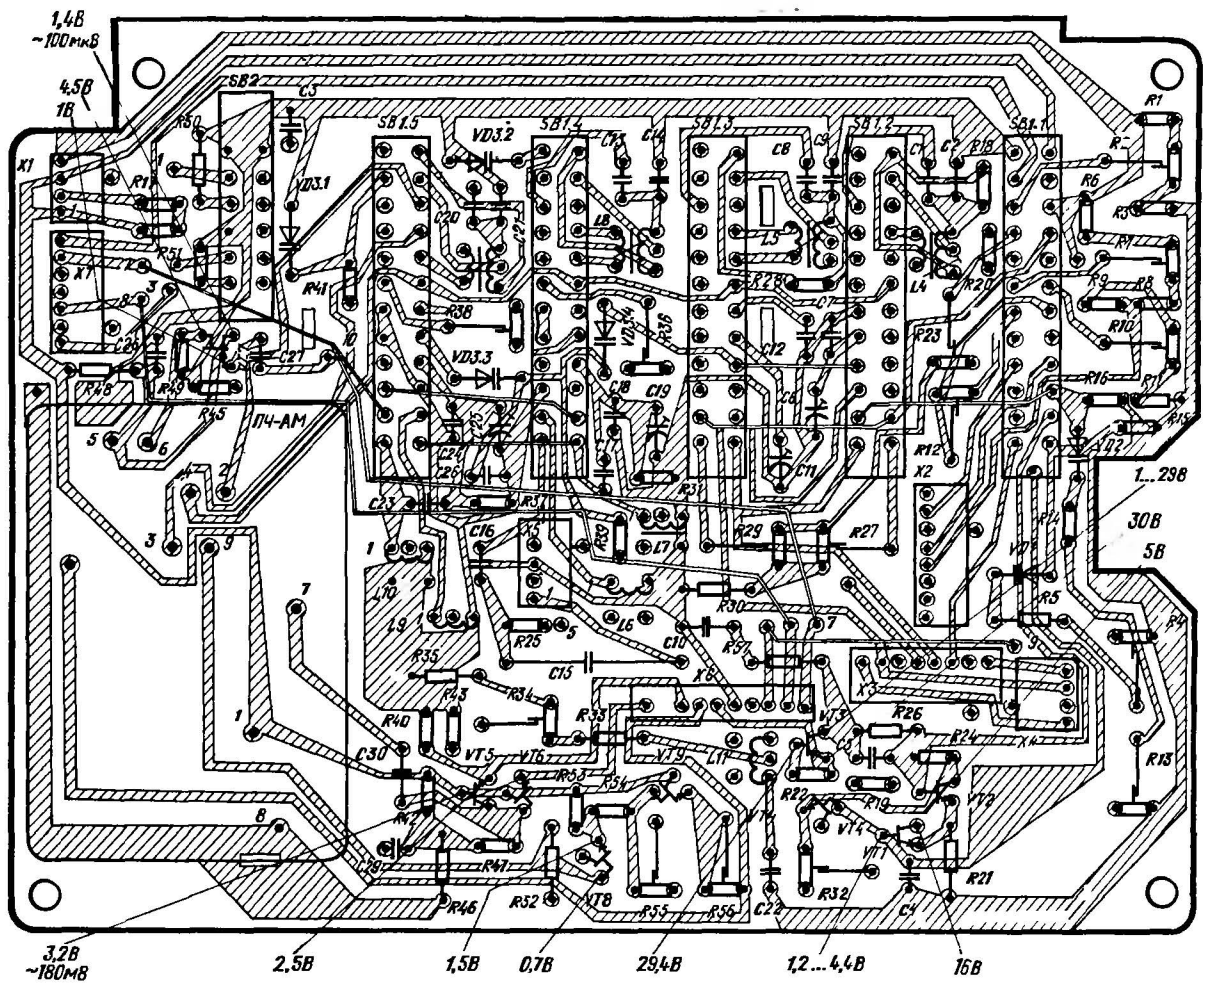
Электромонтажная схема печатной платы блока АМ (А3) магнитолы «Арго РМ-006С» (вид со стороны пайки деталей)
